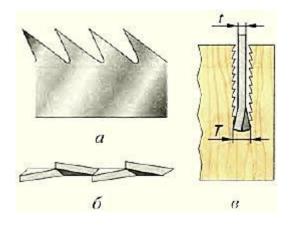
Зубья пилы для продольного пиления: а — форма зубьев; б — вид разведённых зубьев; в — процесс пиления (вид со стороны пласти заготовки)
